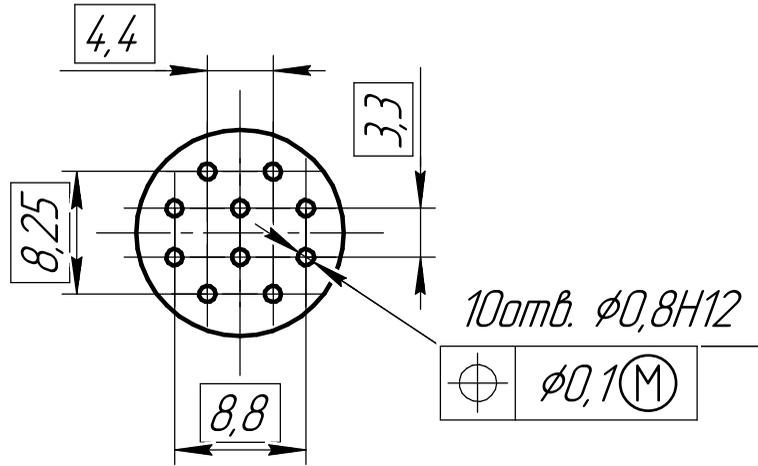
Разметка отверстий для ОСН-25-10/18...П-...
